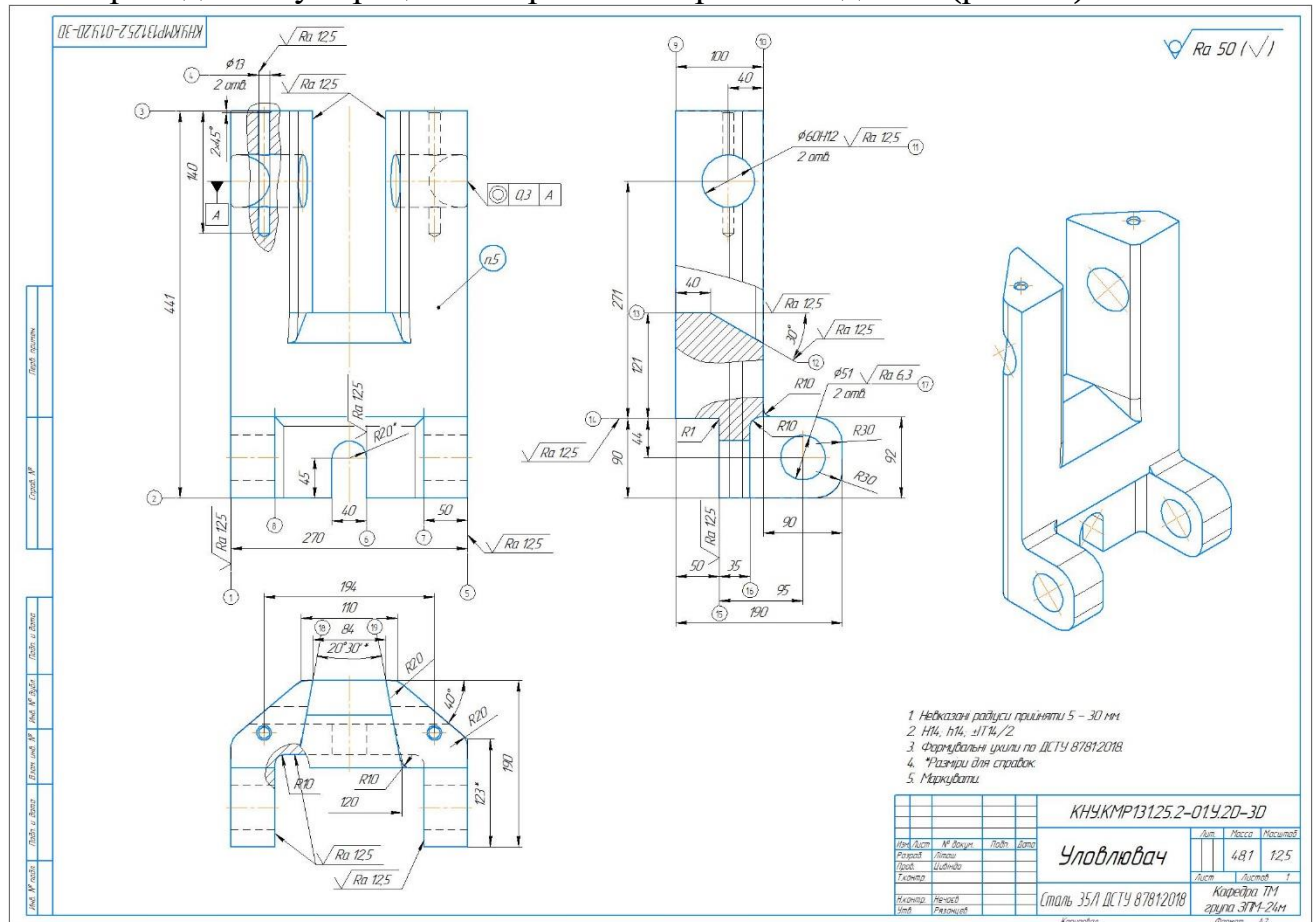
Креслення деталі з розставленими номерами поверхонь
